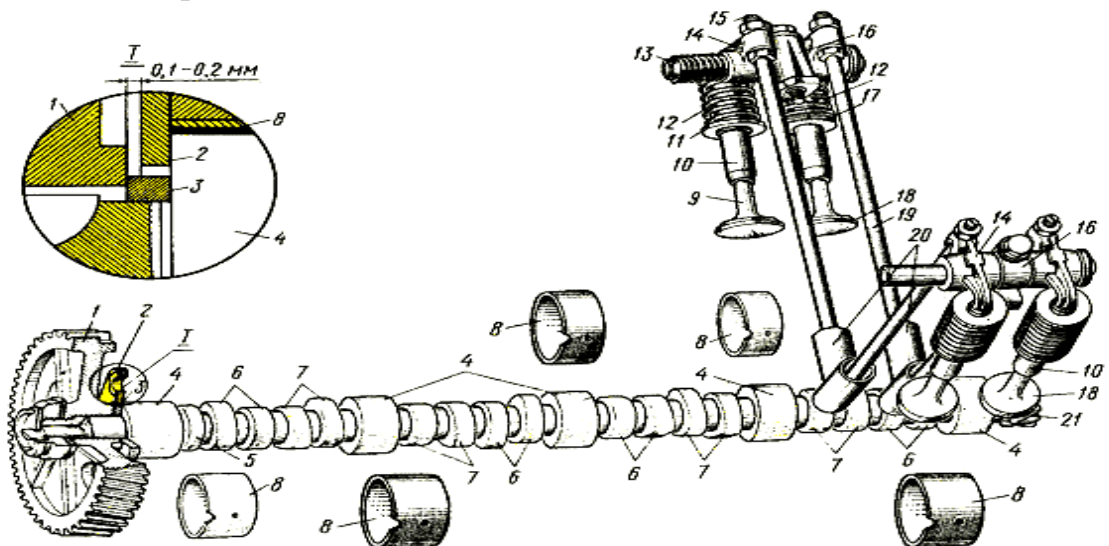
Механізм газорозподілу: 1 - шестерня розподільного валу; 2 - упорний фланець; 3 - розп'ярне кільце; 4 - опорні шийки; 5 - ексцентрик приводу паливного насоса; 6 - кулачки випускних клапанів; 7 - кулачки впускних клапанів; 8 - втулки; 9 - впускний клапан; 10 - напрямна втулка; 11 - наполеглива шайба; 12 - пружина; 13 - вісь коромисел; 14 - коромисло; 15 - регулювальний гвинт; 16 - стійка осі коромисел; 17 - механізм повороту випускного клапана; 18 - випускний клапан; 19 - штанга; 20 - штовхачі; 21 - шестірня приводу масляного насоса і переривника-розподільника.
